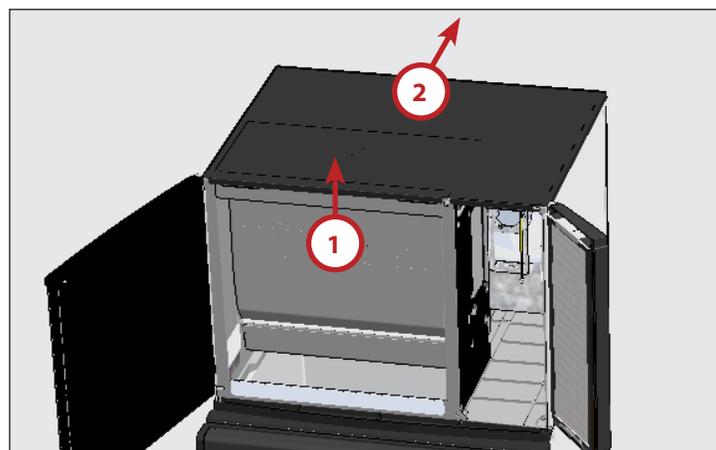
Sollevare il bordo frontale, far scorrere indietro il pannello frontale, quindi sollevarlo per toglierlo.
